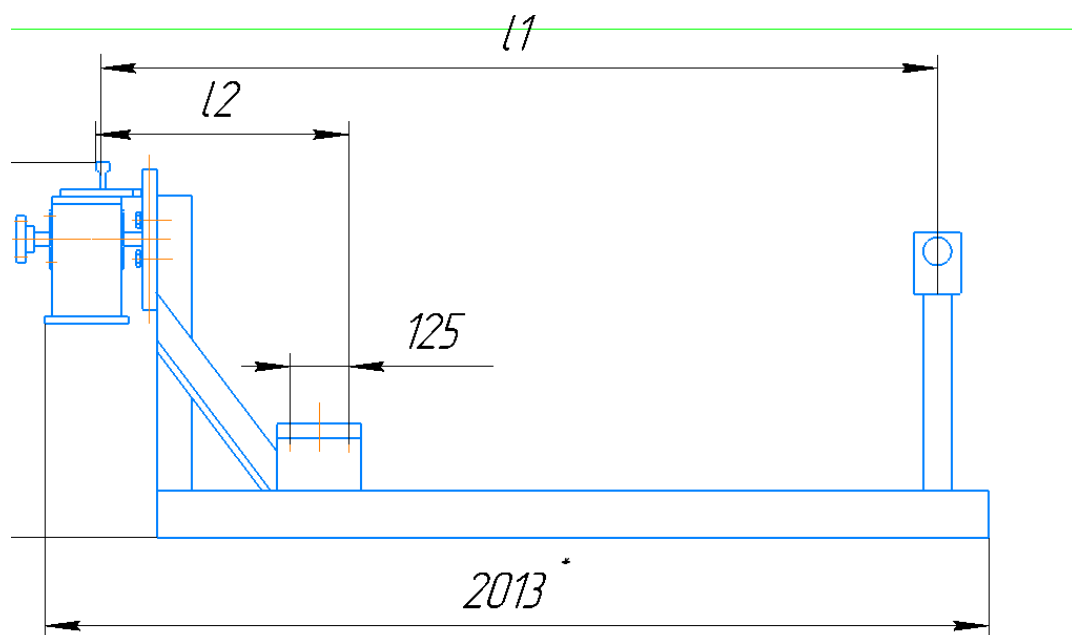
Расчётная схема вала поворотного механизма
